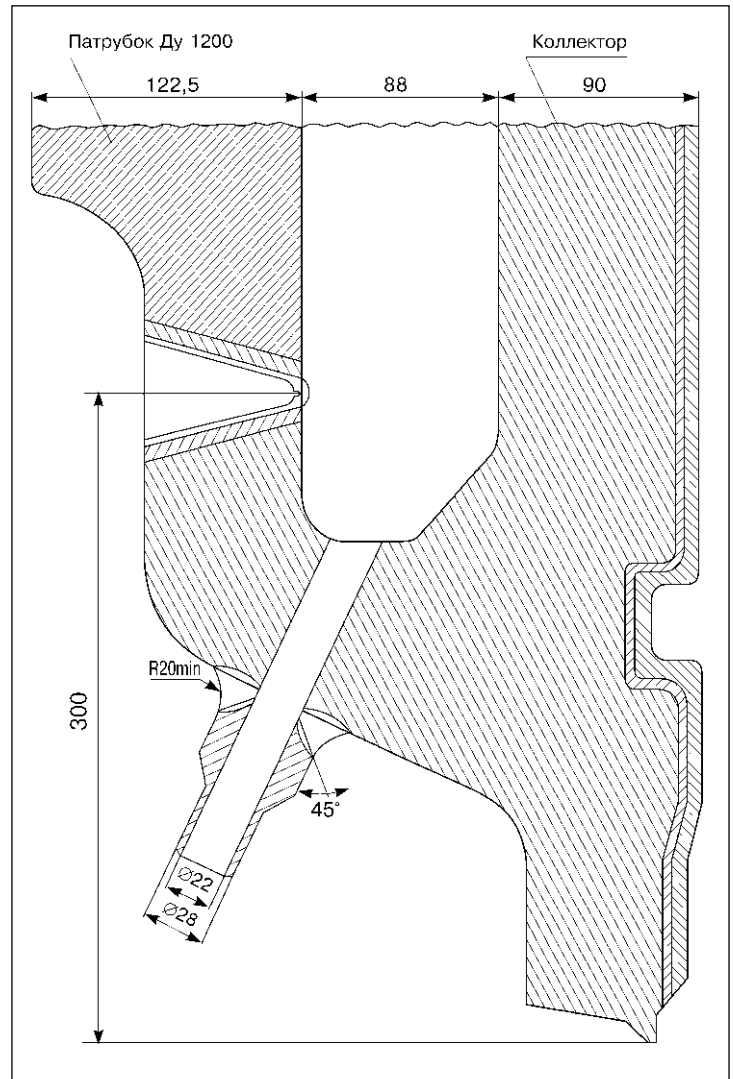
Соляной «карман» и сварное соединение приварки коллектора к патрубку Ду 1200 ПГВ–1000М
